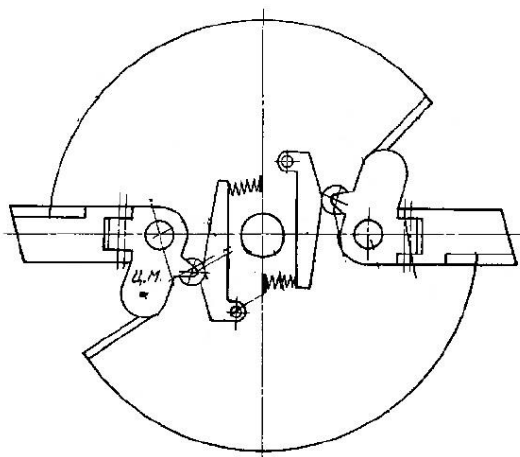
Ножевой подпружиненный шарнирно-сочленённый рабочий орган
